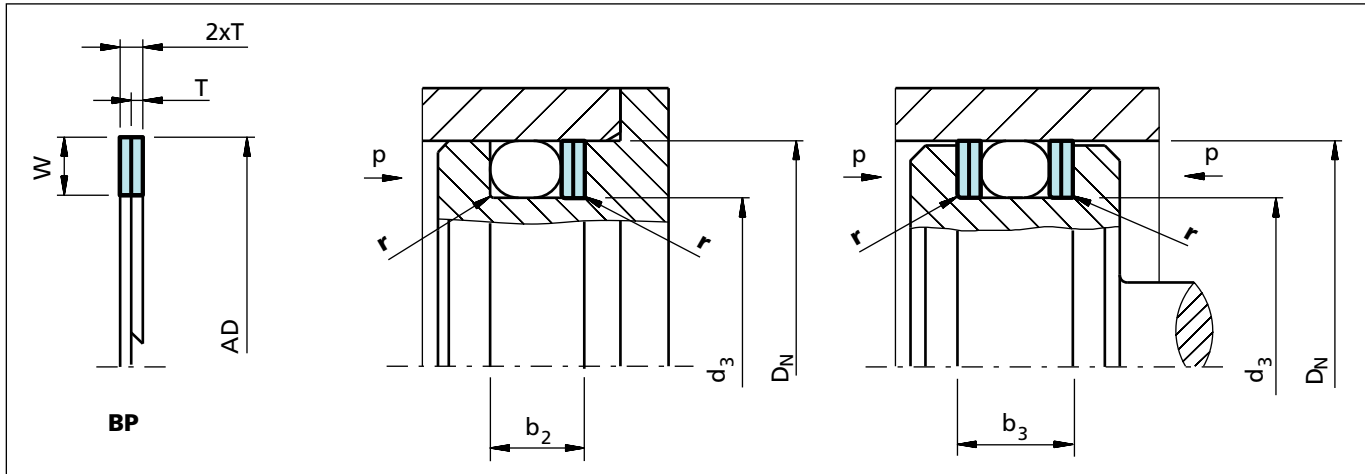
Einbauzeichnung, außendichtend, spiralförmige Stützring Bauform
